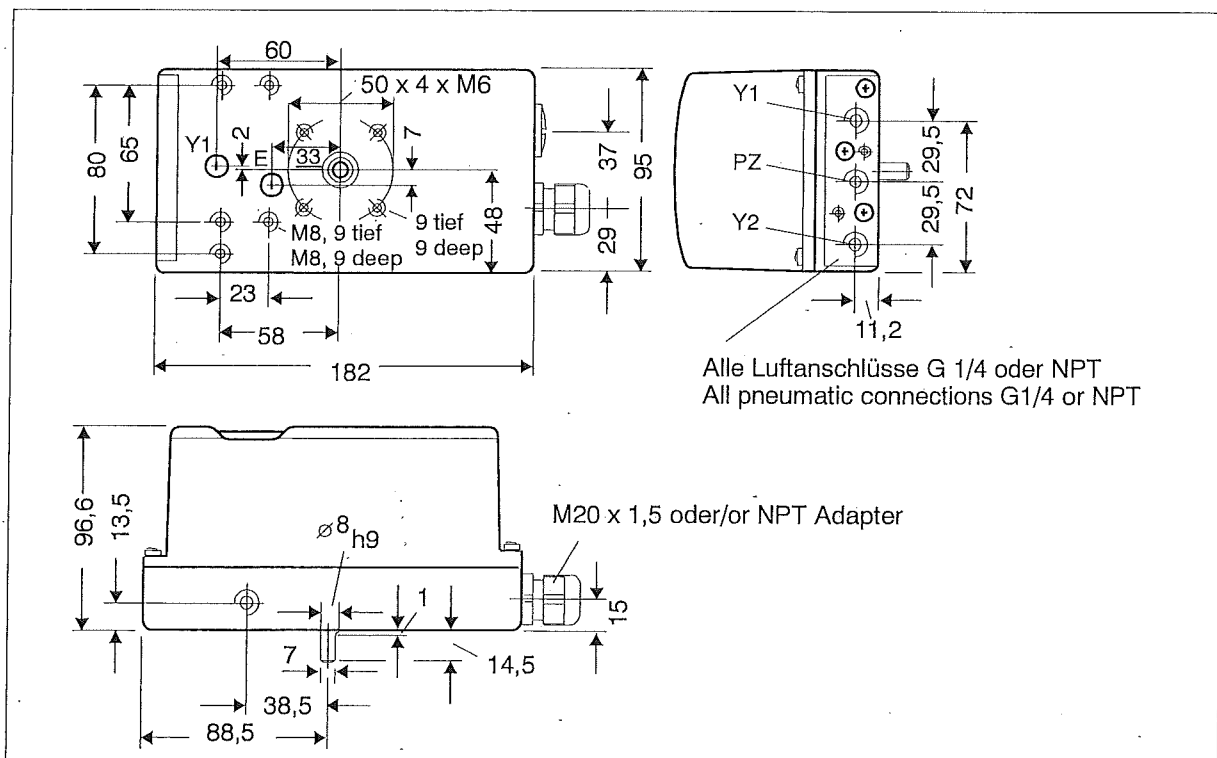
Maßbild Ausführung Kunststoffgehäuse
